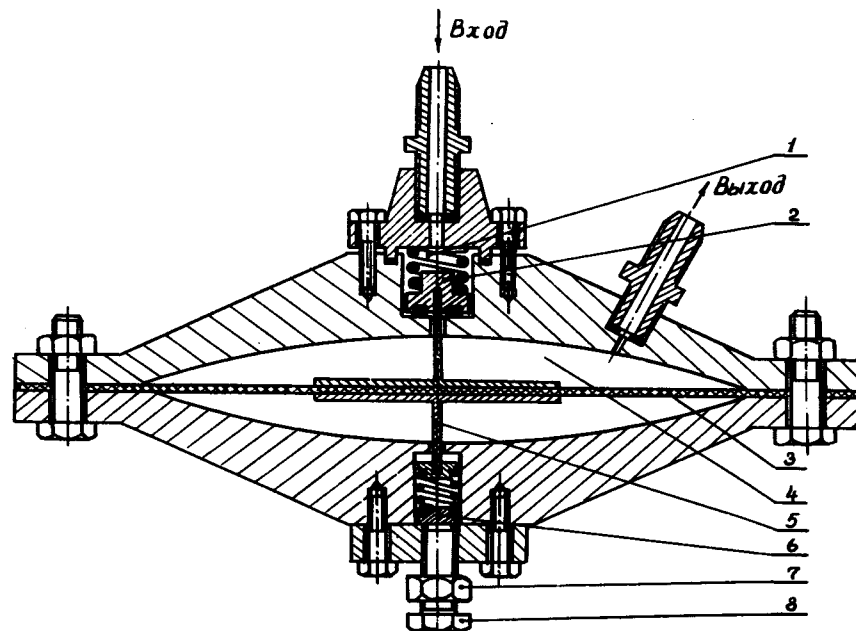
Стабилизатор давления, 1 - главная пружина; 2 - клапан давления; 3 - резиновая мембрана; 4 - рабочая камера; 5 - толкатель; 6 - устройство с пружиной; 7 - контргайка; 8 - регулирующий болт.
